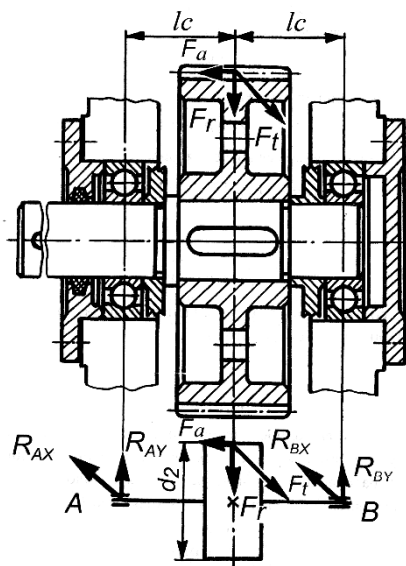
Подшипниковые узлы ведомого вала цилиндрического косозубого редуктора
